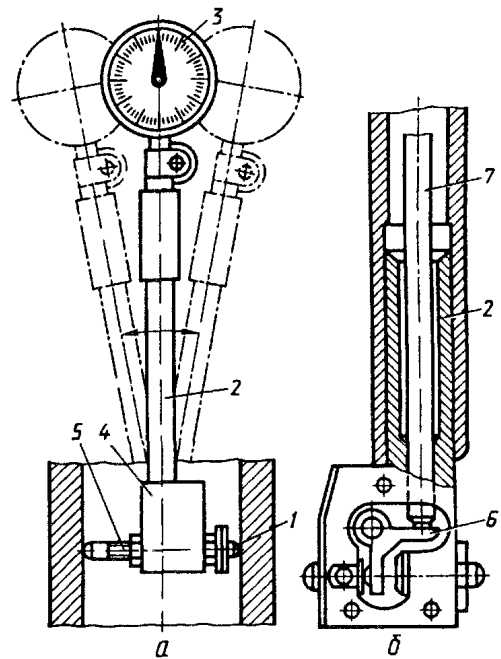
Індикаторний нутромір: а - схема контролю отвору; б - важільний механізм; 1 - шуп; 2 - штанга; 3 - індикатор; 4 - коробка важеля; 5 - гвинт попередньої наладки; 6 - важіль; 7 - шток
